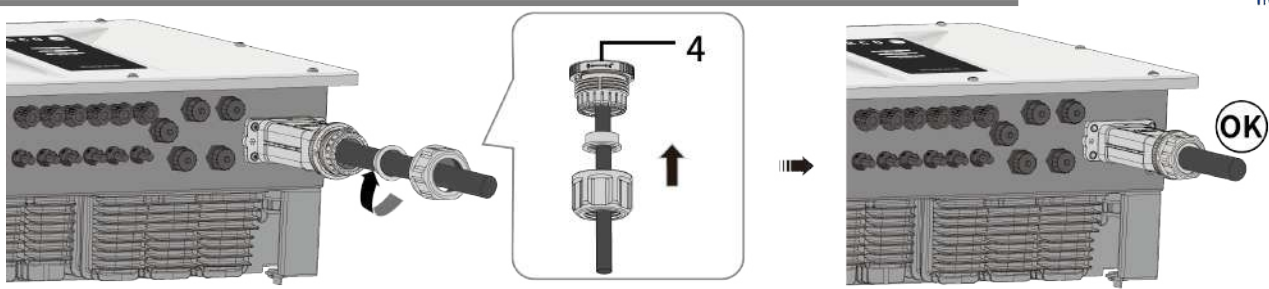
AC-Abdeckung aufsetzen und Mutter festschrauben.
